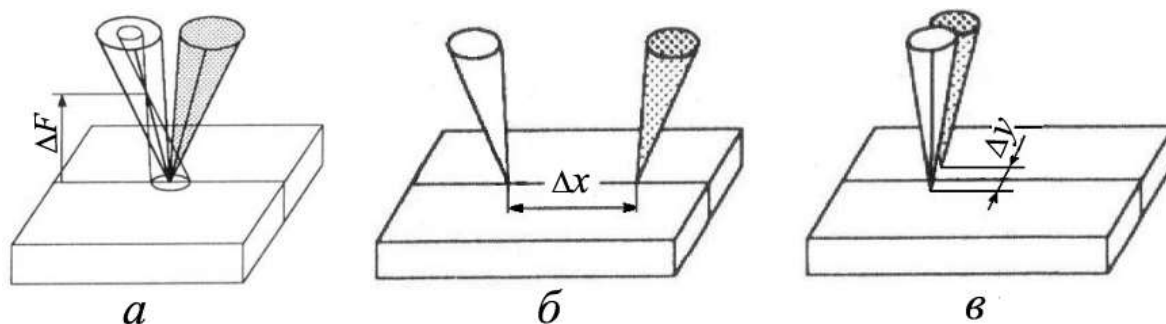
Різні схеми двопроменевого лазерного зварювання
